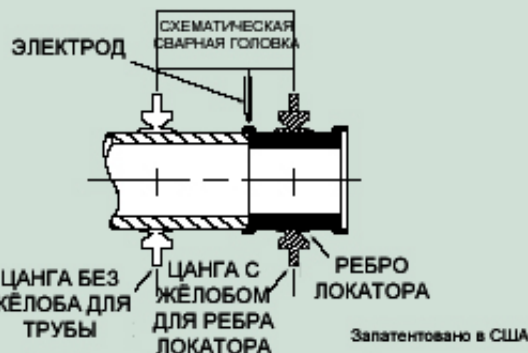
Вращающийся сварочный электрод находится в пределах стационарной головки и вращается на 360° для получения однородных точных швов.
